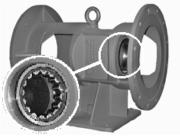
Опора подшипника, наружное кольцо подшипника с цилиндрическими роликами
